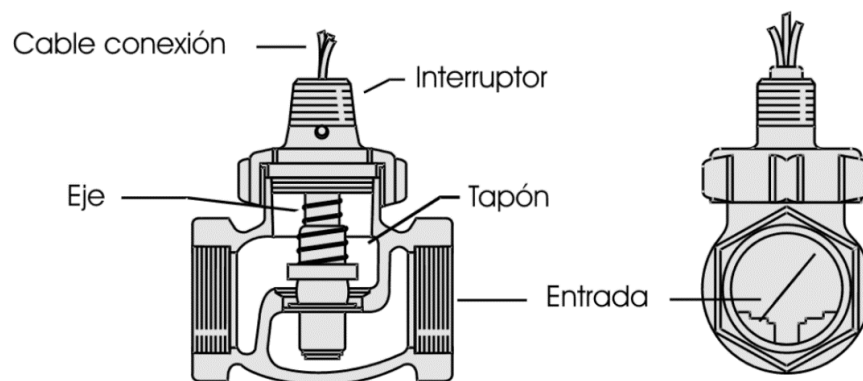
Поплавково-пружинний витратомір з вертикально розміщеним поплавцем
